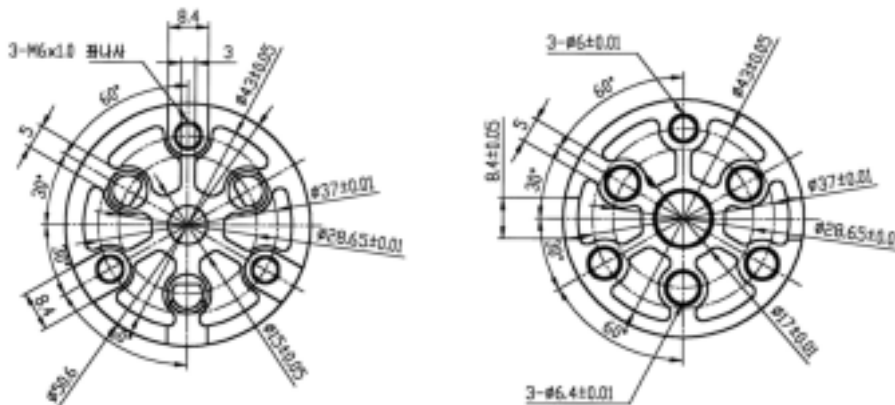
하단안내집합체(Bottom Guide Assembly) 부품도
